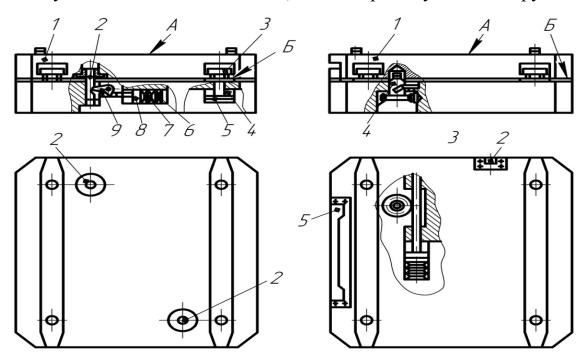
Устройство для базирования и закрепления спутников гибких производственных систем: 1 – спутник; 2 – фиксатор; 3 – зажимные планки; 4, 7 – пружины; 5, 6 – гидроцилиндры; 8 – поршень; 9 – рычаг
